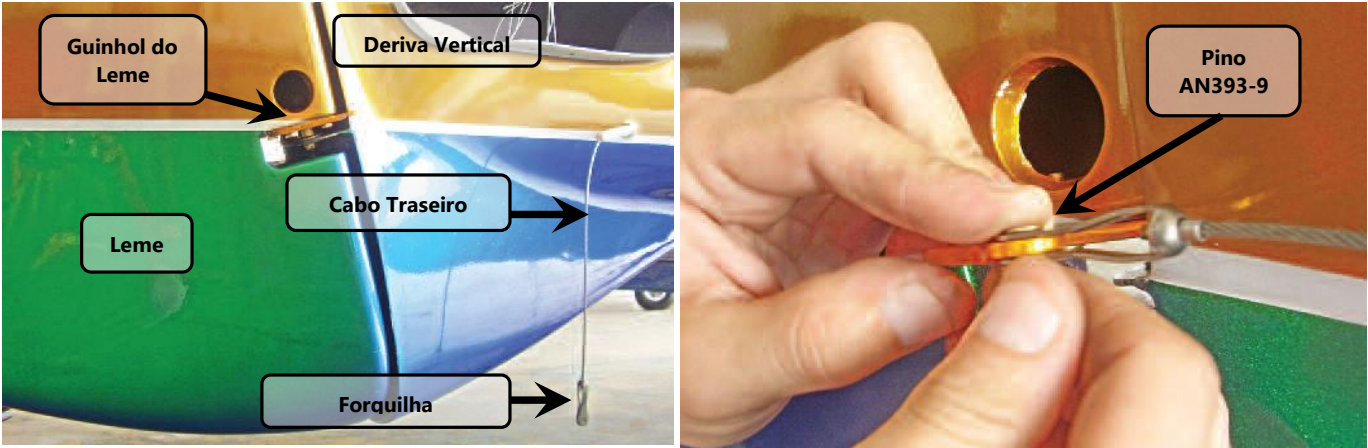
Instalação do cabo AA-10-10-6000 no guinhol do leme.
